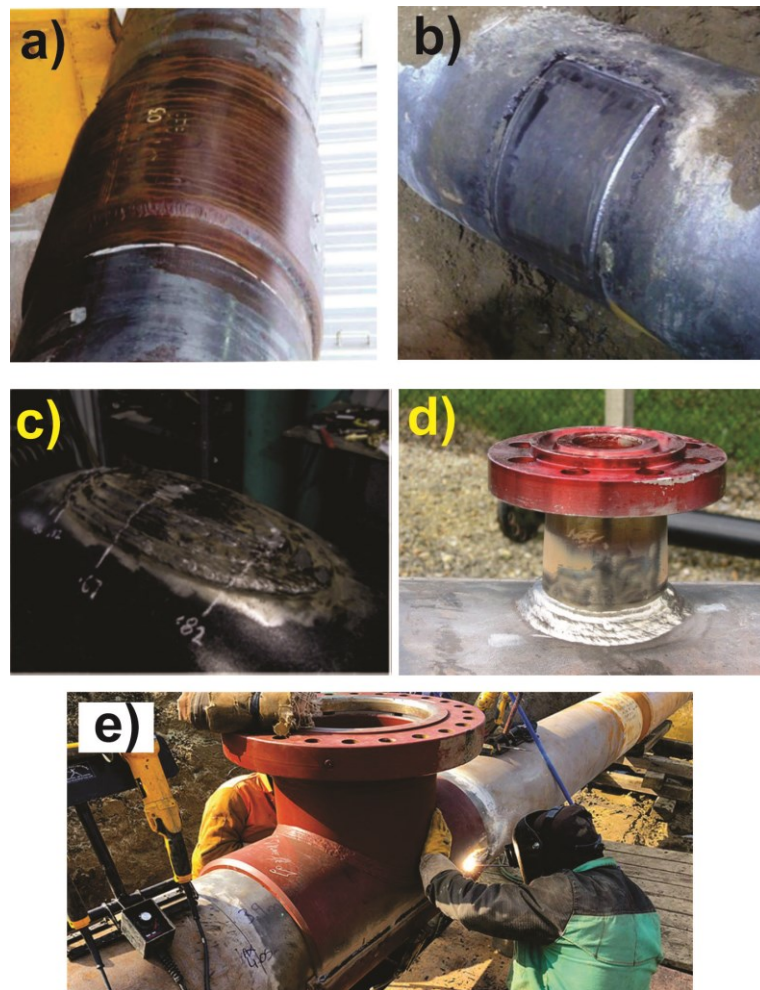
Aplicações de soldagem *in-service* para reparos e instalações. Em a) Dupla-calha tipo B soldada; b) Remendo local (*patch*) soldado; c) Depósito de solda direta sobre a superfície (*weld overlay*); d) Soldagem de derivação; e) Soldagem de *fitting* para trepanação. Fonte: Pesquisa na internet pelo tema *in-service welding*.
